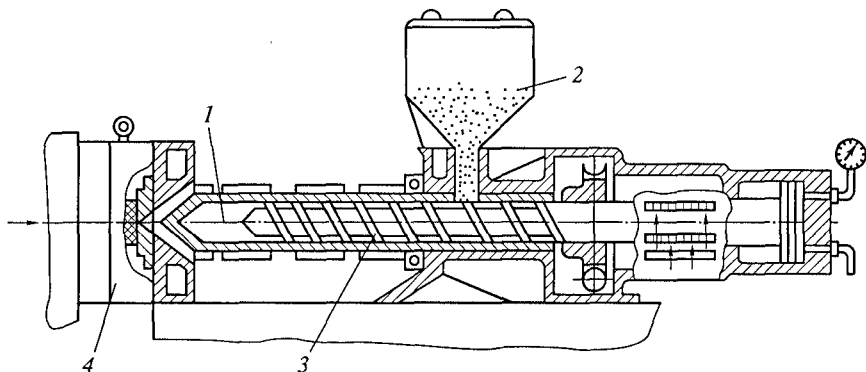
Схема установки для изготовления пенополистироловых моделей под давлением:
